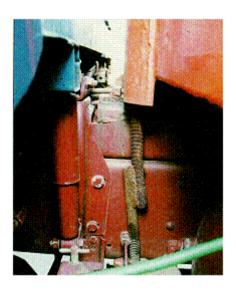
Kranbefestigung durch ungeeignete und unsachgemäß geschweißte Briedenschraube
